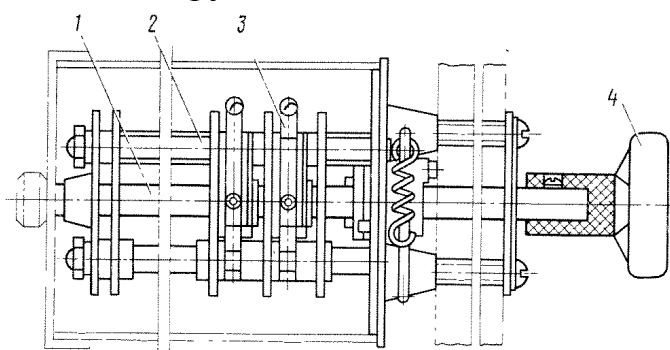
Разъединитель цепей управления УП5316-Е139
